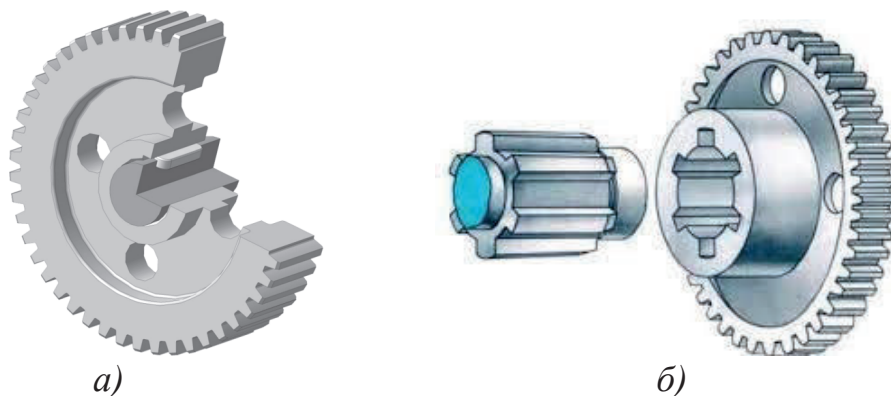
Види з'єднань деталей: а – шпонкове; б – шліцеве
